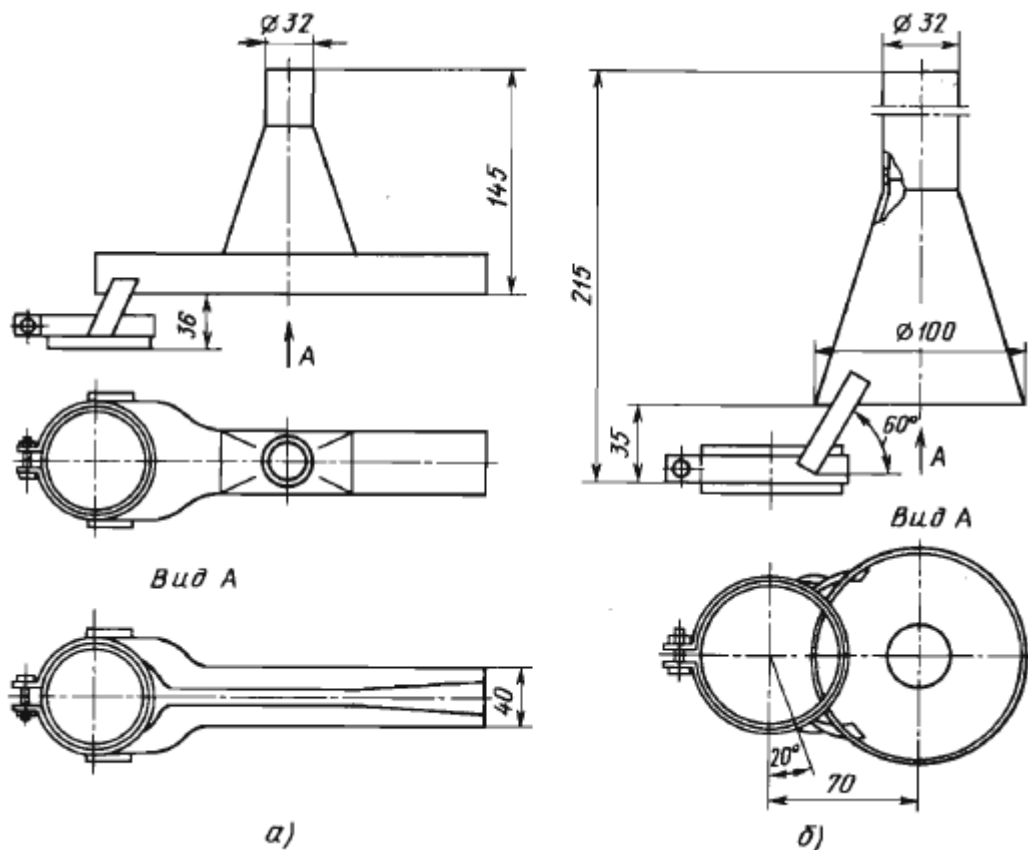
Повітроприймачі для зварювання під флюсом
